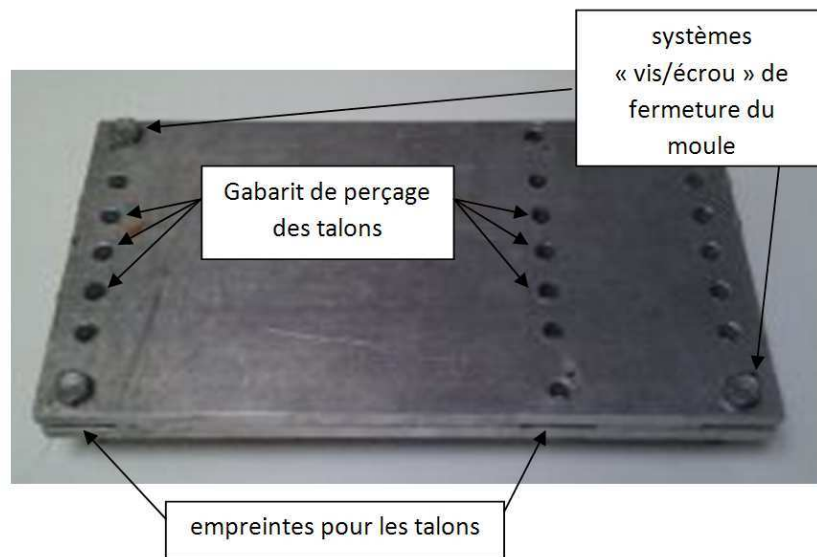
Moule pour éprouvette de Bias Test (fermé)
